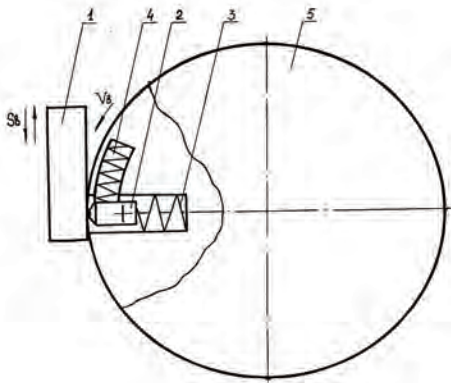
Схема выглаживания вращающимся инструментом: 1 – деталь; 2 – выглаживающие наконечники; 3 – основная пружина; 4 – дополнительная пружина; 5 – корпус
